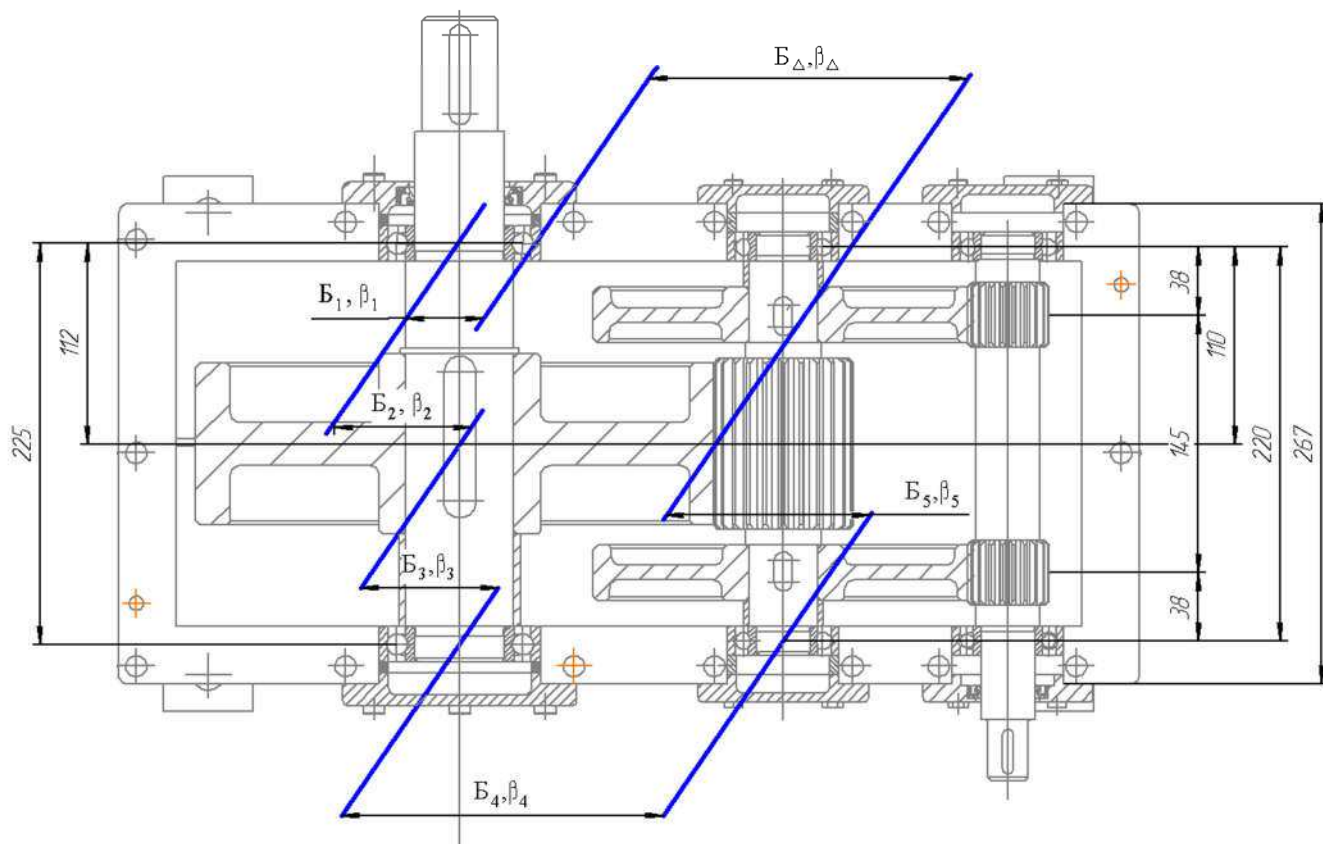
Размерная цепь цилиндрической зубчатой передачи (тихоходная ступень)
